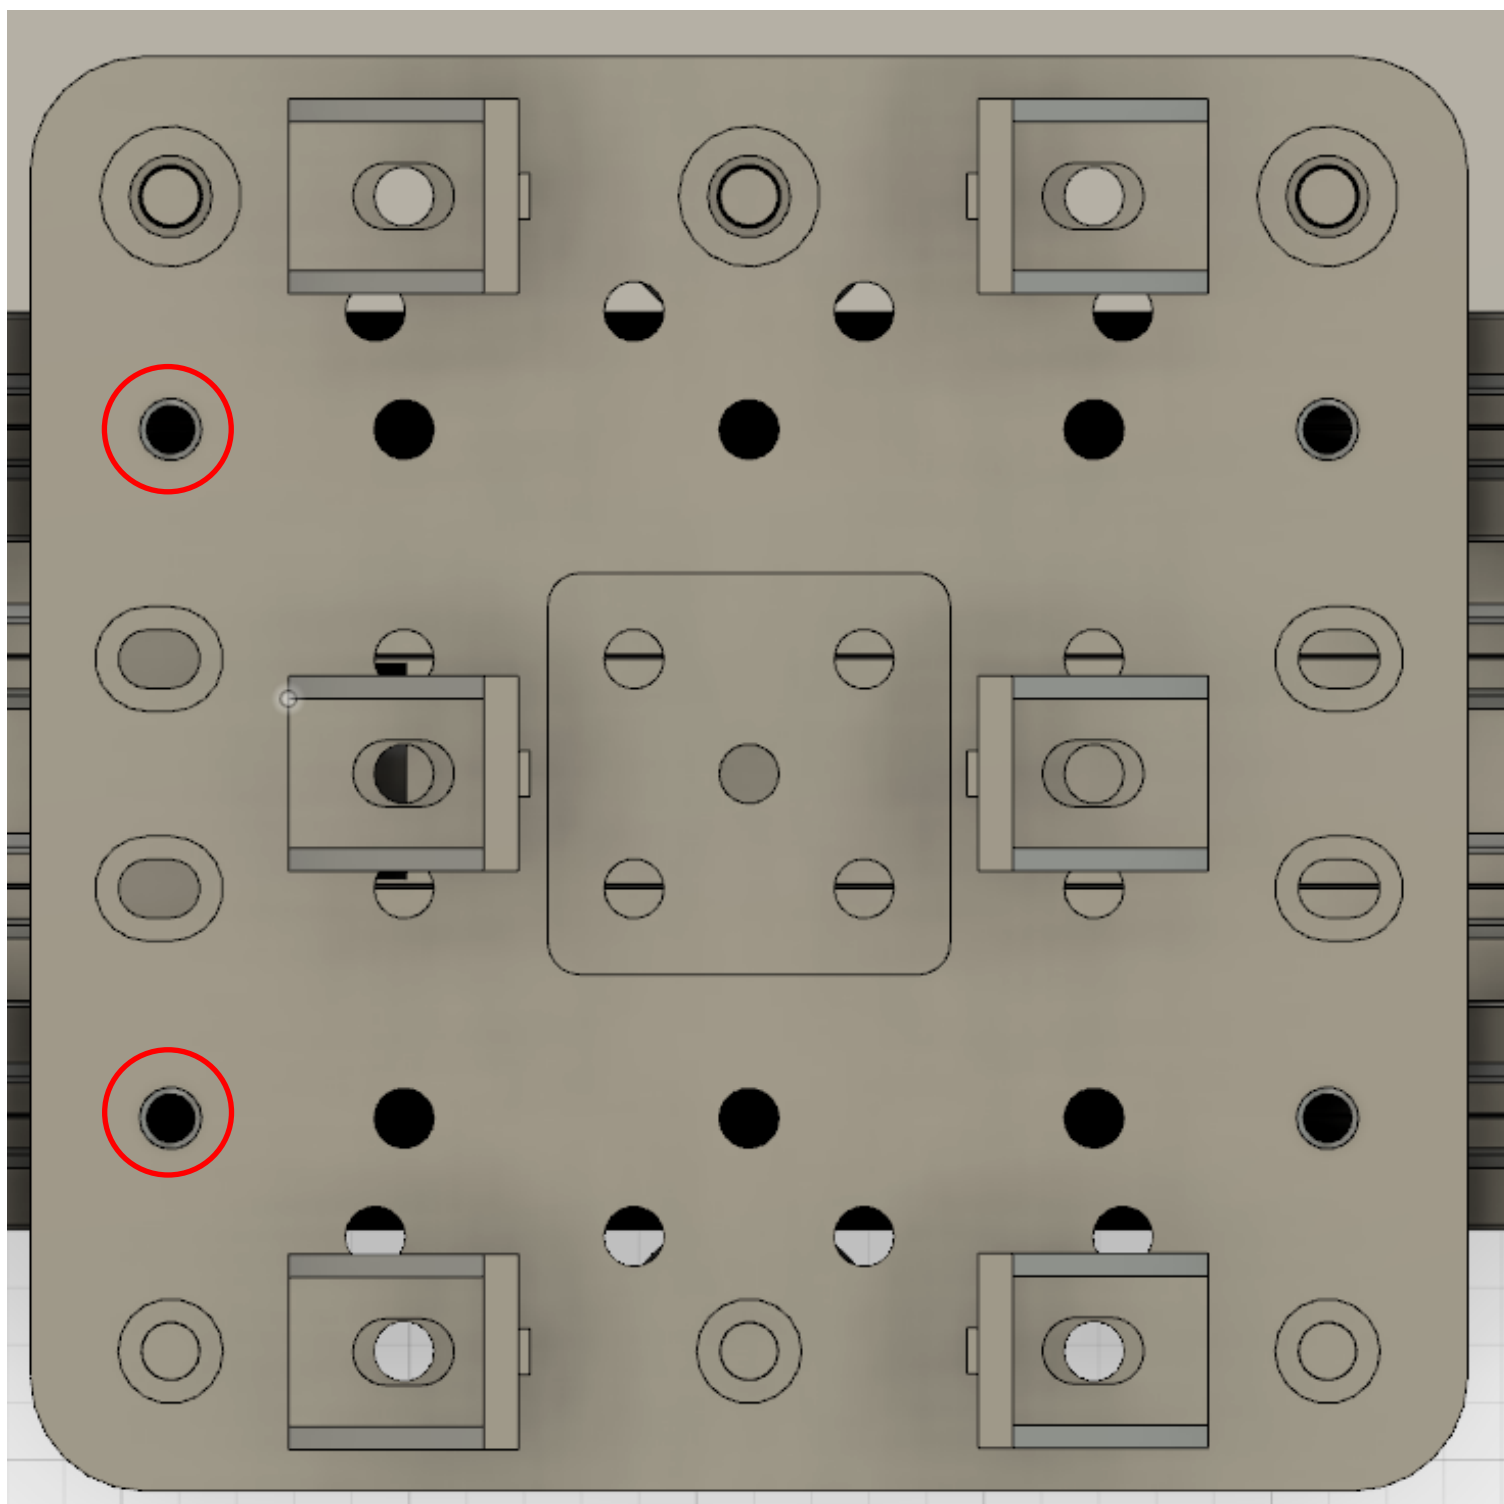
Die Gantryplate mit den Löchern, welche ihr bohren müsst (5mm). Also in die Teile, die ich gefräst habe
